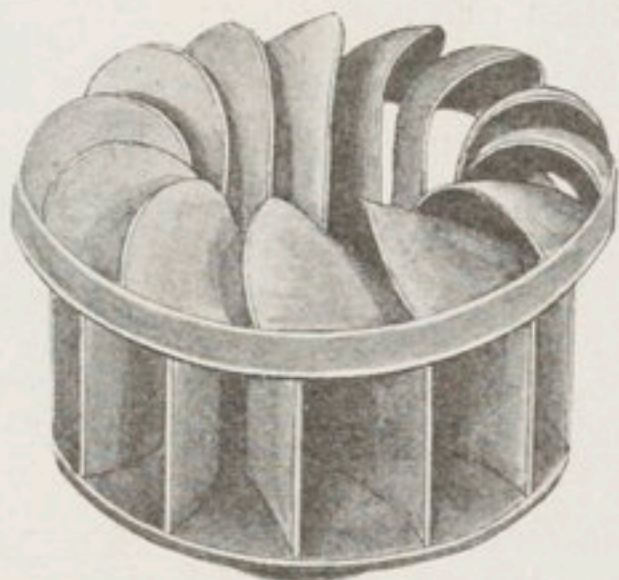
Roue de turbine Hercule-Progrès coulée d'une seule pièce.
